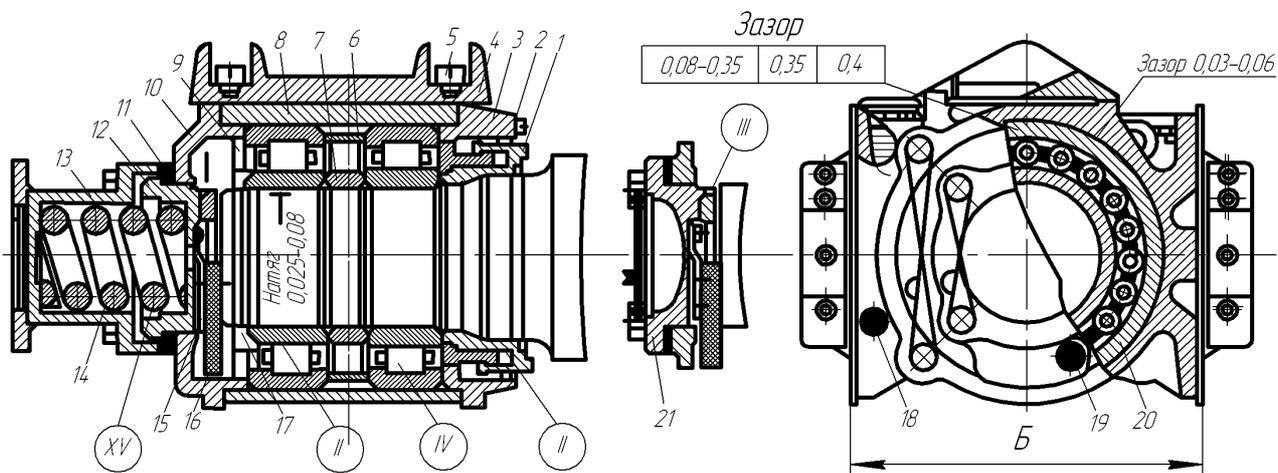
Букса колесной пары тепловоза: 1 – лабиринтовое кольцо; 2 – предохранительная планка; 3 – задняя крышка; 4 – арка; 5 – опора балансира; 6, 7 – дистанционные кольца; 8 – корпус буксы; 9 – разделительная диафрагма; 10 – передняя крышка; 11 – регулировочная прокладка; 12 – осевой упор; 13 – крышка; 14 – пружина; 15 – пластинчатая пружина; 16 – войлочный фитиль; 17 – стопорное кольцо; 18, 19 – пробки для заполнения твердой и жидкой смазки; 20 – роликоподшипник; 21 – осевой упор средней колесной пары
